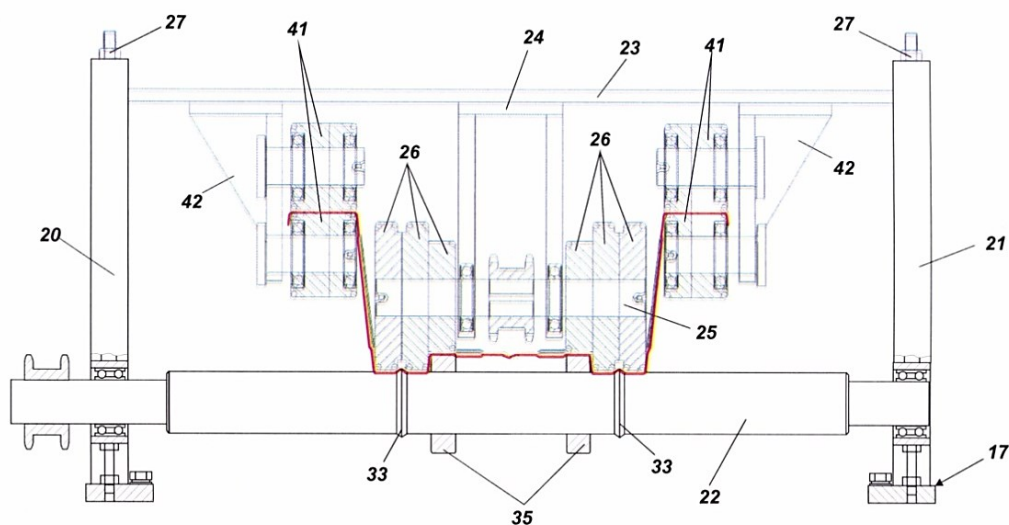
Фрагмент многоклетьевого профилегибочного стана изготовления профиля [5]:
